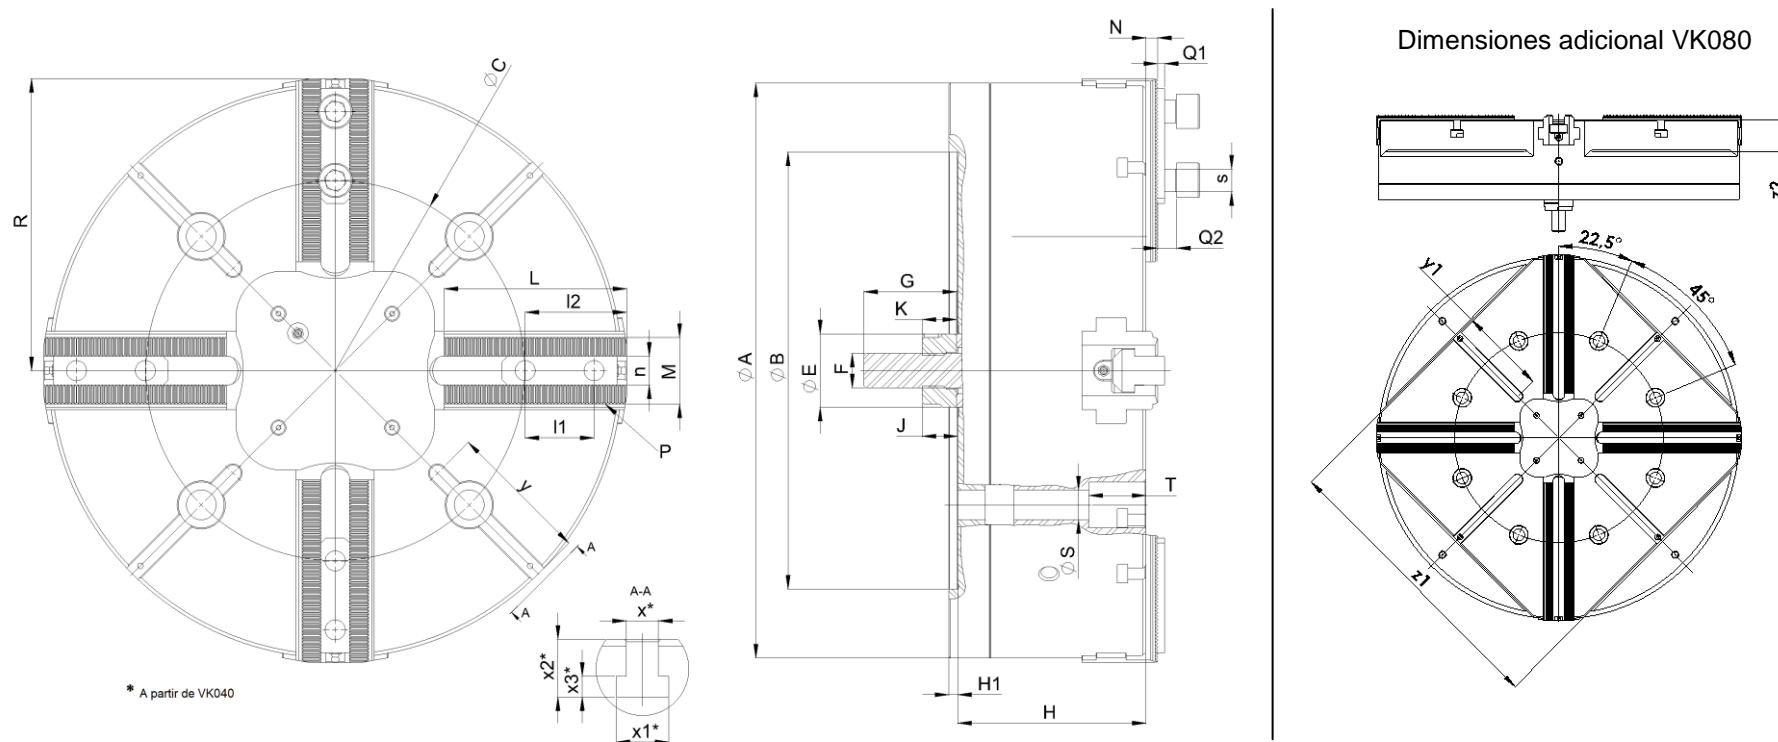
Dimensiones del sistema de conexión VK021 - VK080
